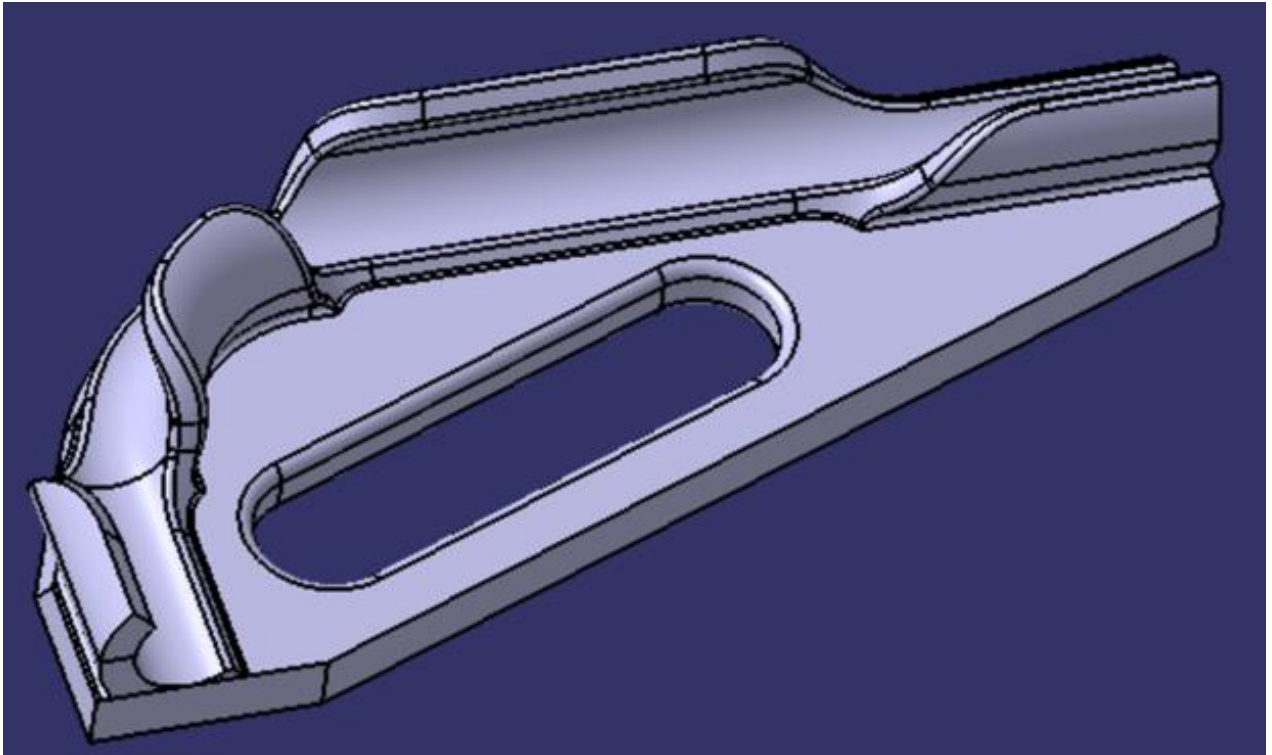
29 Diseño final del molde de flexión 3D en CATIA
